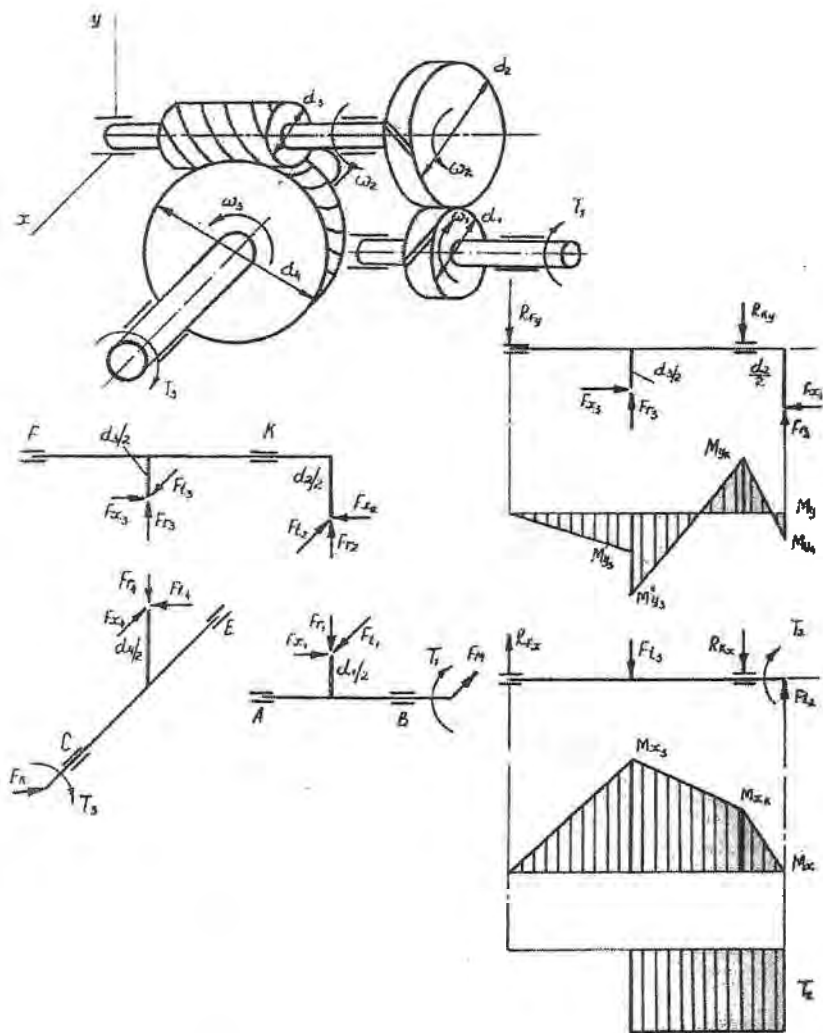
Зубчато-червячная передача с первой цилиндрической косозубой ступенью.
